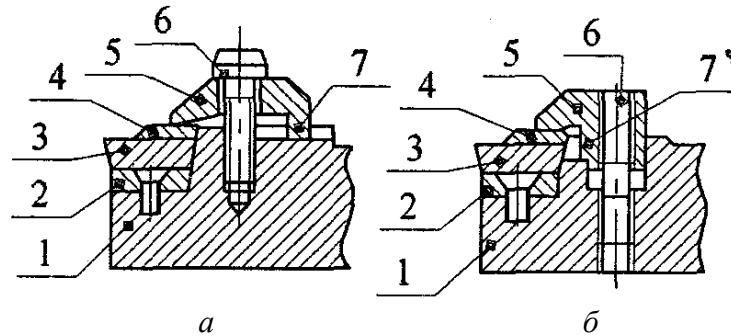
Кріплення пластин до корпусу інструменту:
